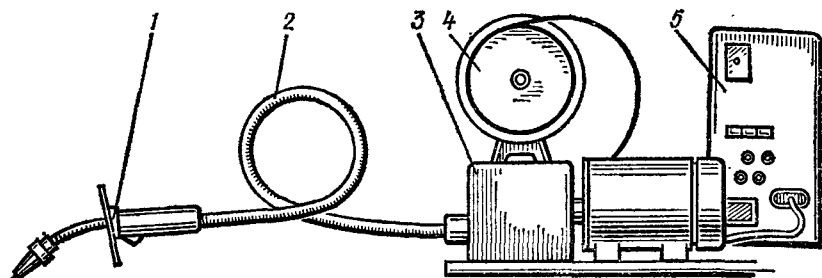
Полуавтомат для дуговой сварки:
